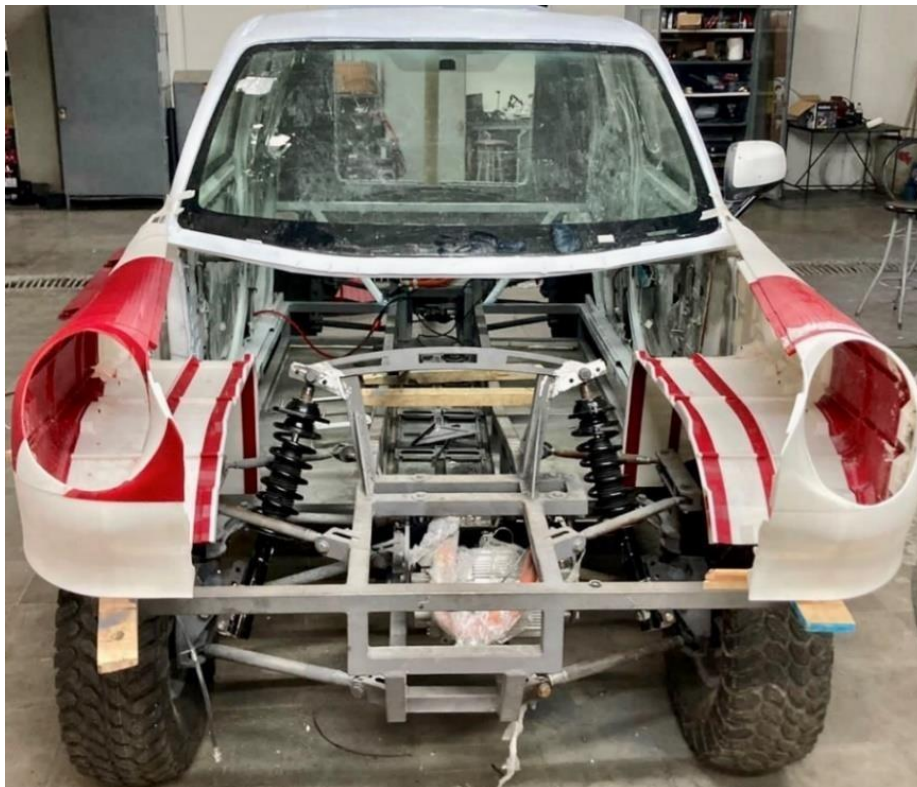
Ensamble completo del sistema de suspensión delantero en el prototipo.
